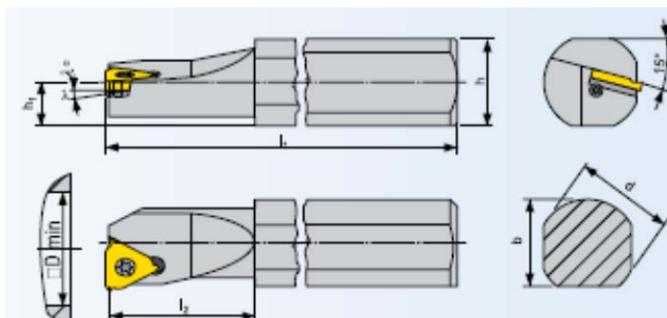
Токарный резец для нарезания внутренней резьбы
